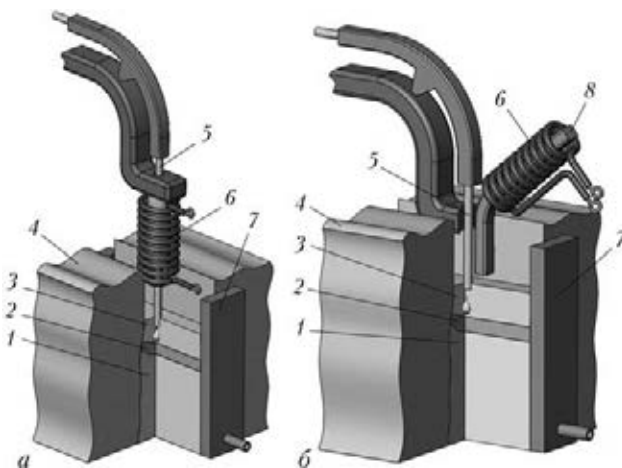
Схемы введения продольного магнитного поля посредством соленоида, расположенного в зоне сварки (*a*), и стержневого магнитопровода (*б*): 1 — сварной шов; 2 — металлическая ванна; 3 — шлаковая ванна; 4 — свариваемый образец; 5 — проволока; 6 — электромагнитная система; 7 — водоохлаждаемая формирующая планка; 8 — магнитопровод
